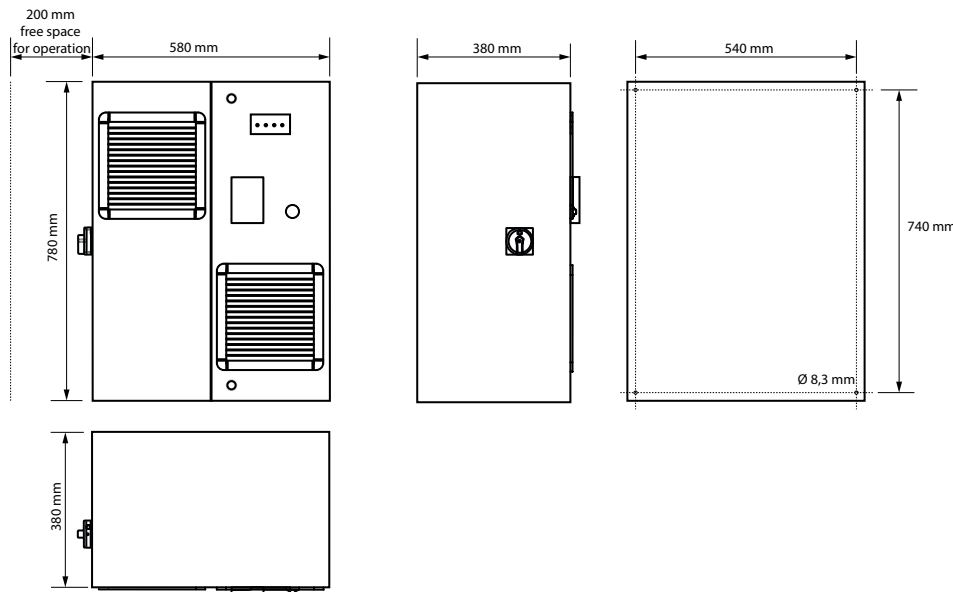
Baugröße BG580 für direkte Wandmontage (FrigoPack FU+ Kälteumrichter im Steuerschrank)
